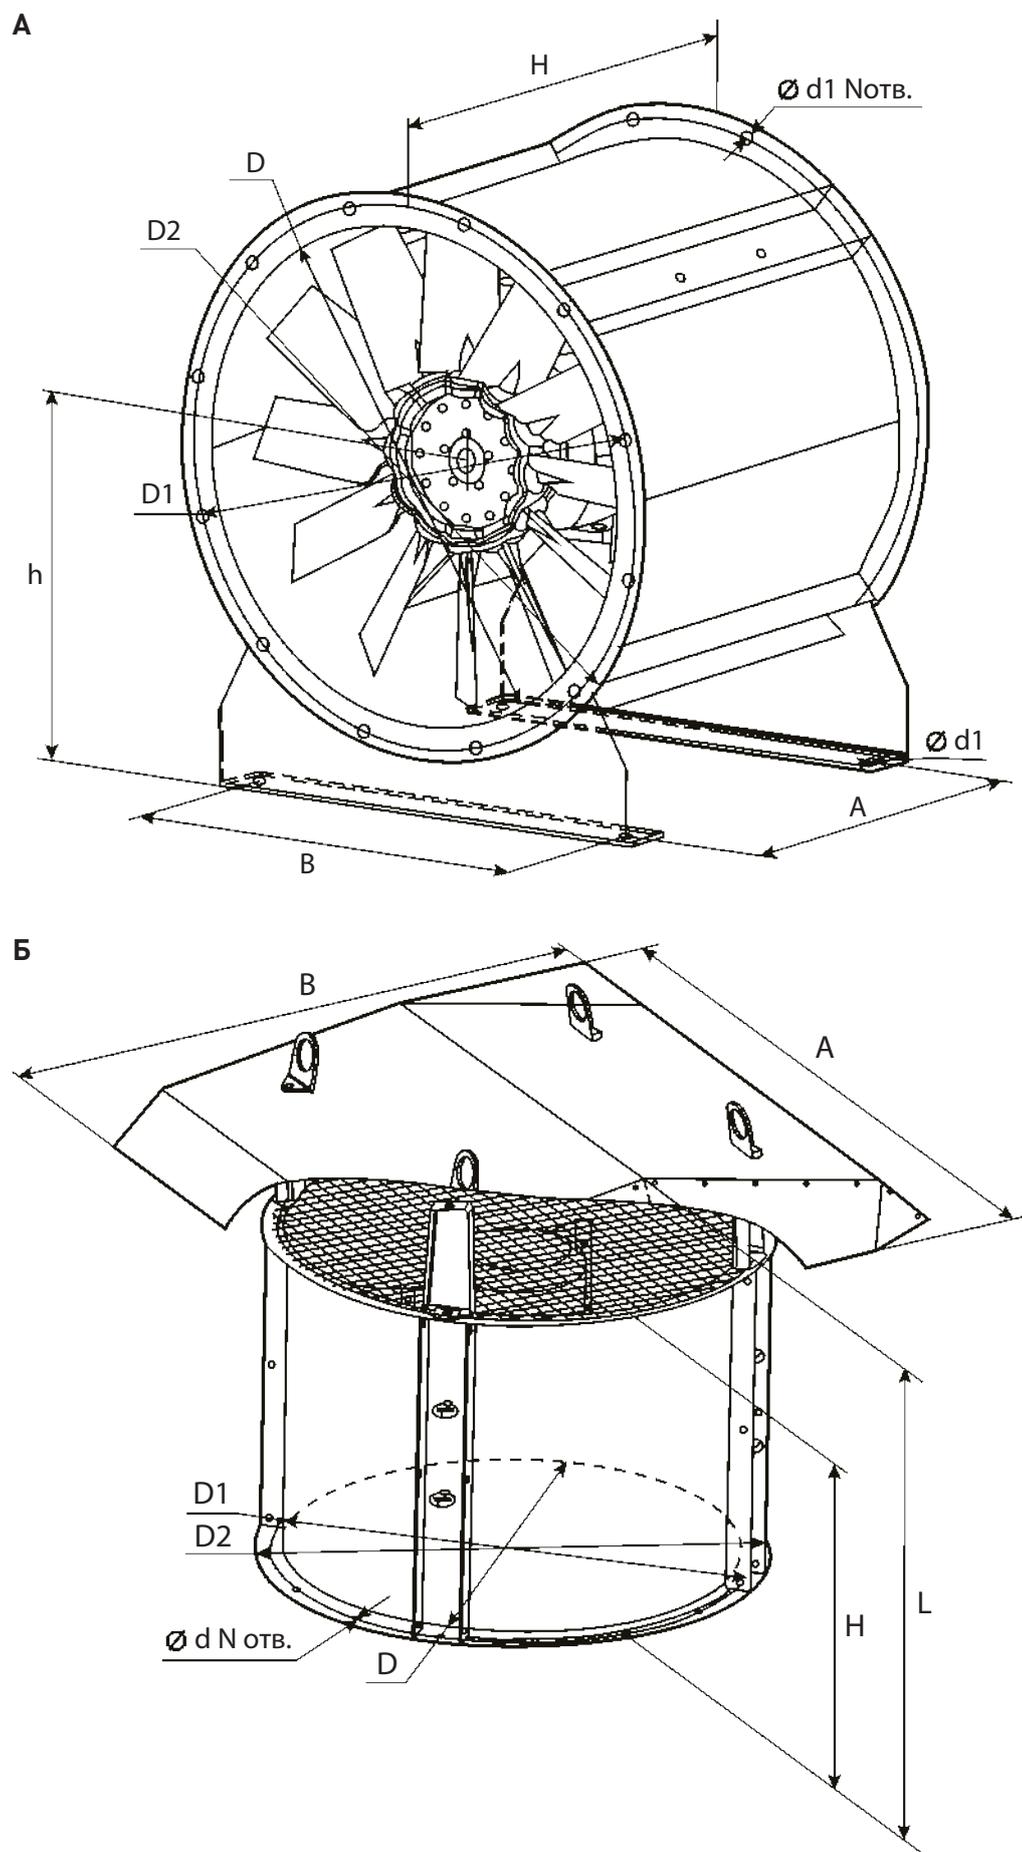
Осевой вентилятор: А – на монтажных опорах; Б – с крышей
